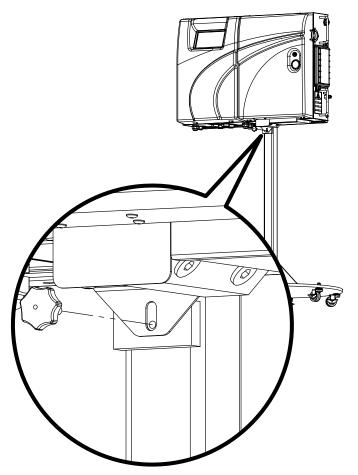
Bodenhalterung des Schmelzgerätes am Standfuß befestigen
